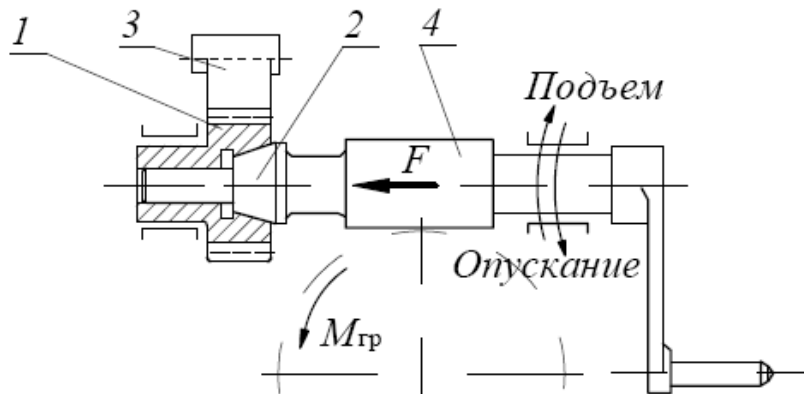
Грузоупорный тормоз с червячной передачей
